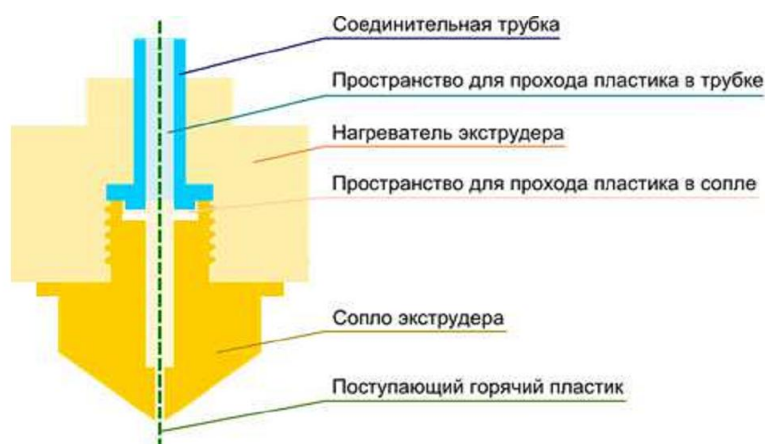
Схема расположения сопла и соединительной трубки в нагревательном блоке экструдера
